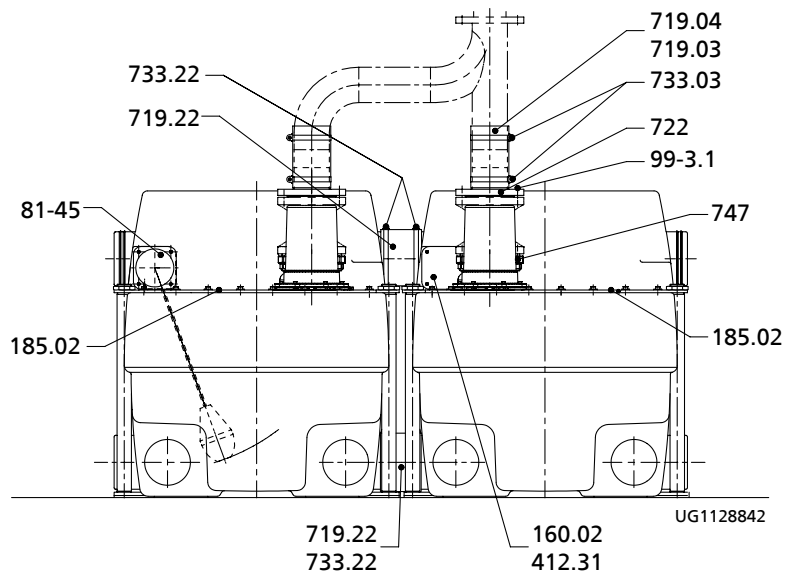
Сборочный чертеж Compacta UZ900 с 2 резервуарами
